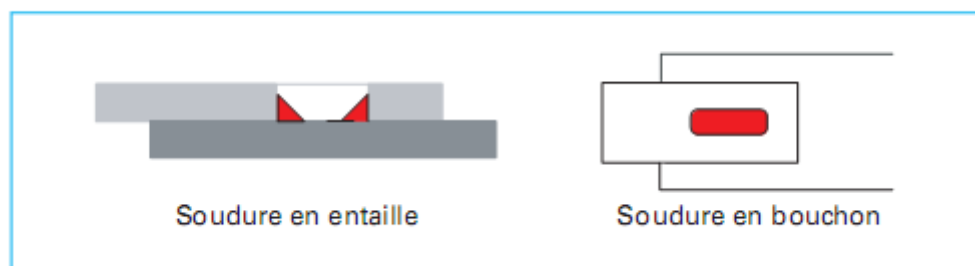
Soudure en bouchon et en entaille[57].
